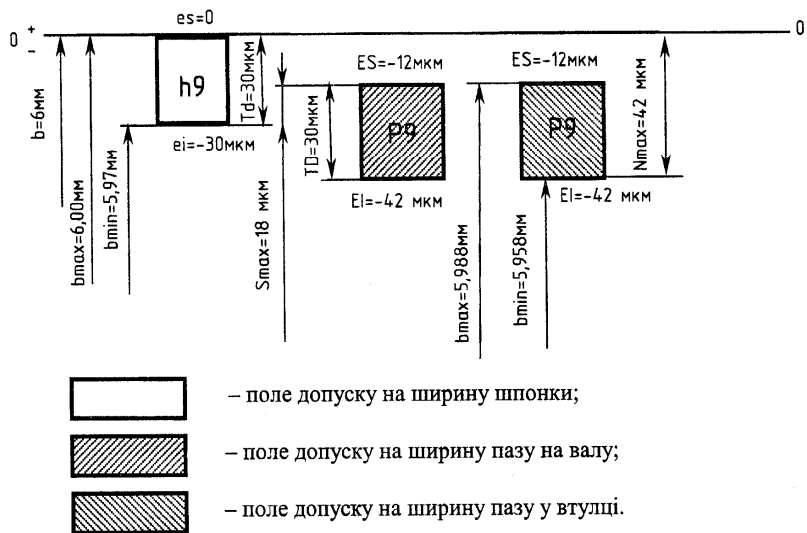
Схема розташування полів допусків на бічну поверхню деталей з'єднання сегментною шпонкою:
